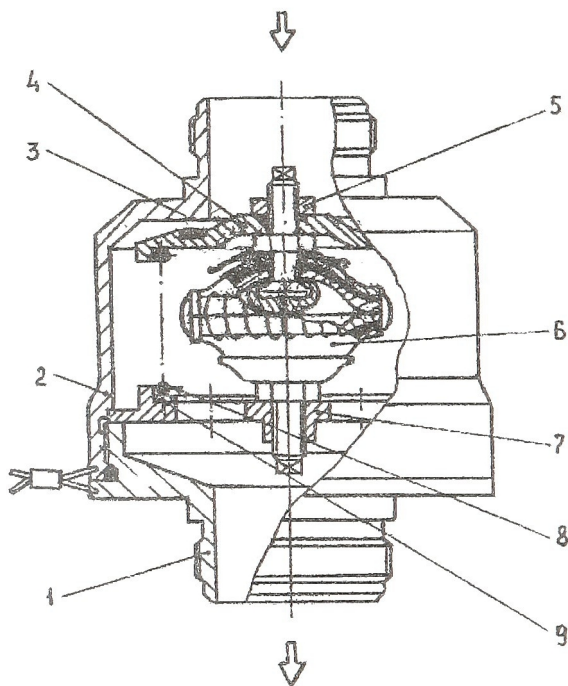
Предохранительный клапан низкого давления с подвеской золотника на виброизоляторе
